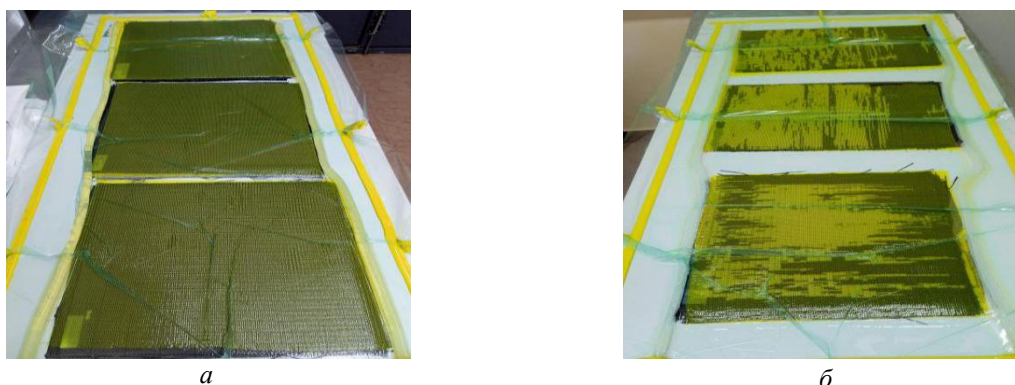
Формовка заготовок: а – без дефекта формования; б – с дефектом формования
